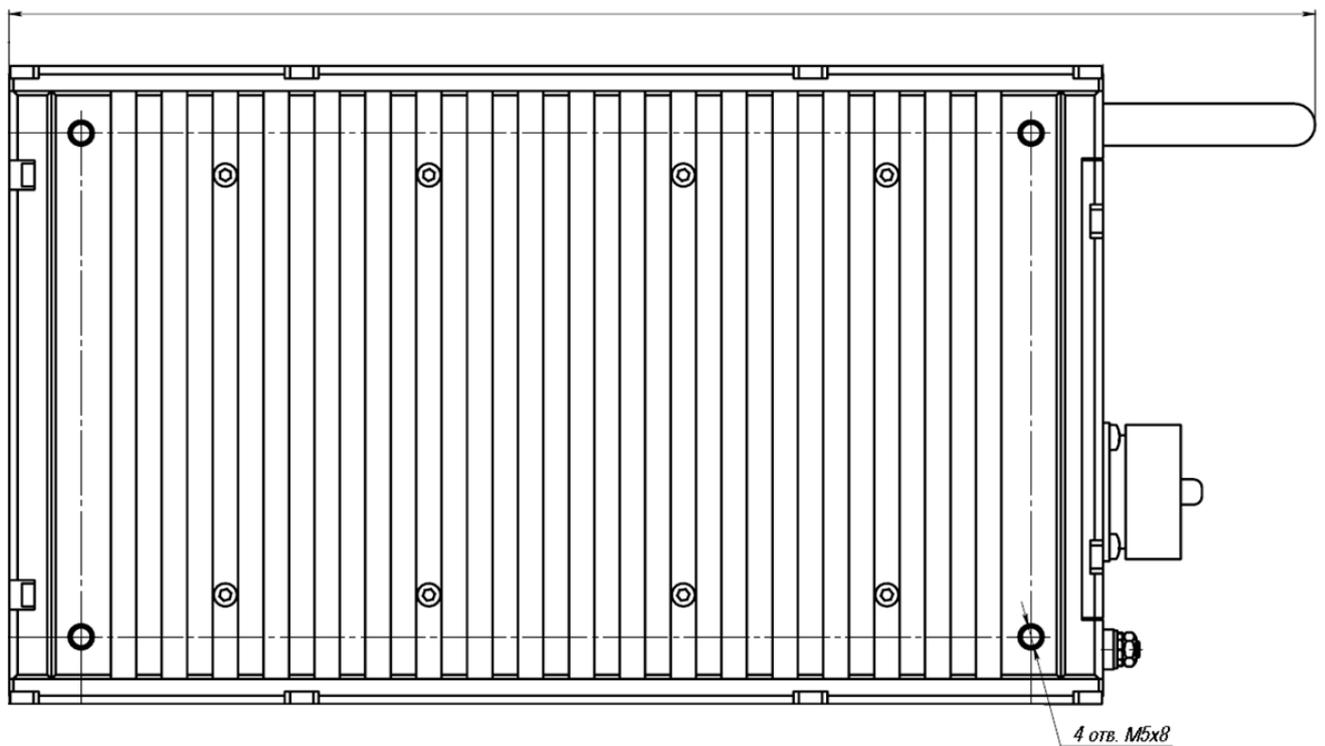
2 - Габаритные размеры ICC300 (вид слева)
